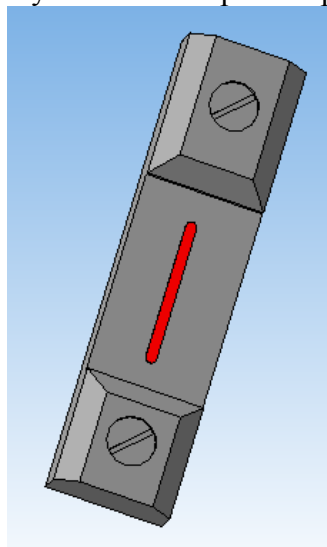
Сборочная 3D-модель контролирующего элемента
